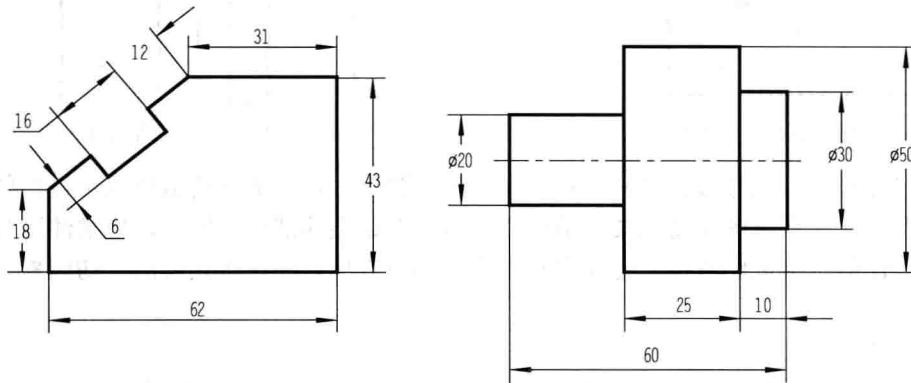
非水平方向线性尺寸的尺寸数字标注
